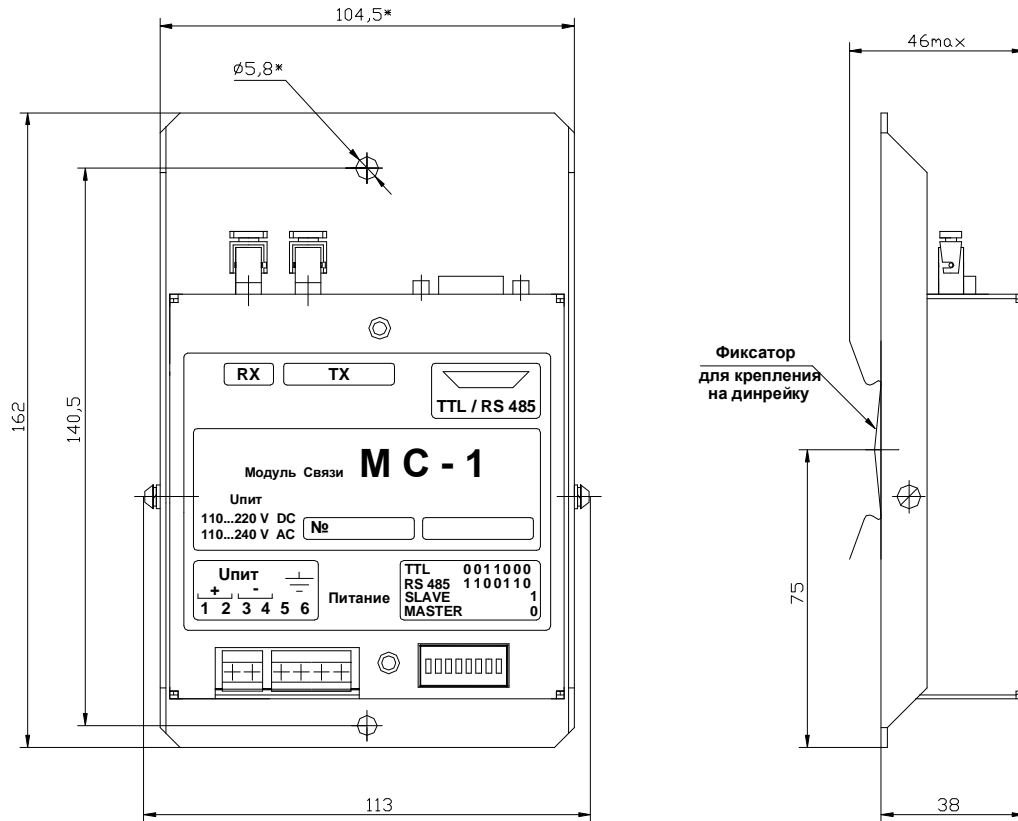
Внешний вид, габаритные и установочные размеры модуля
